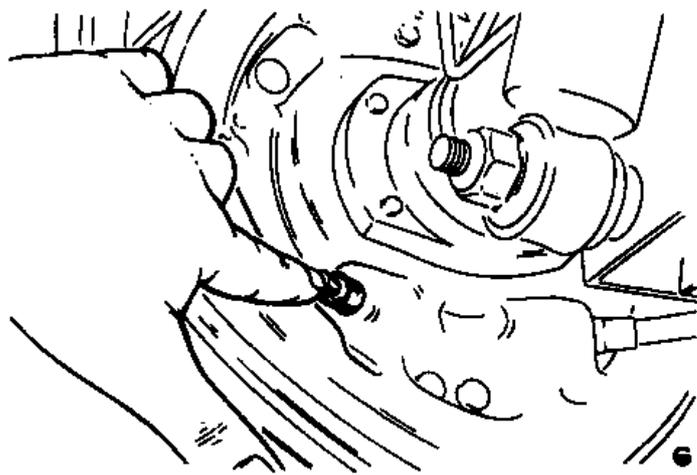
Регулировочный плунжер задних колес (Разд.12)
